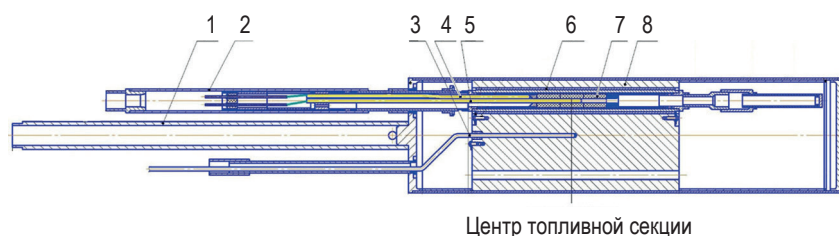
Эскиз капсулы: 1 – тяга; 2 – твэл; 3 – 5 – термопары; 6 – гафниевый экран; 7 – таблетка; 8 – корпус
